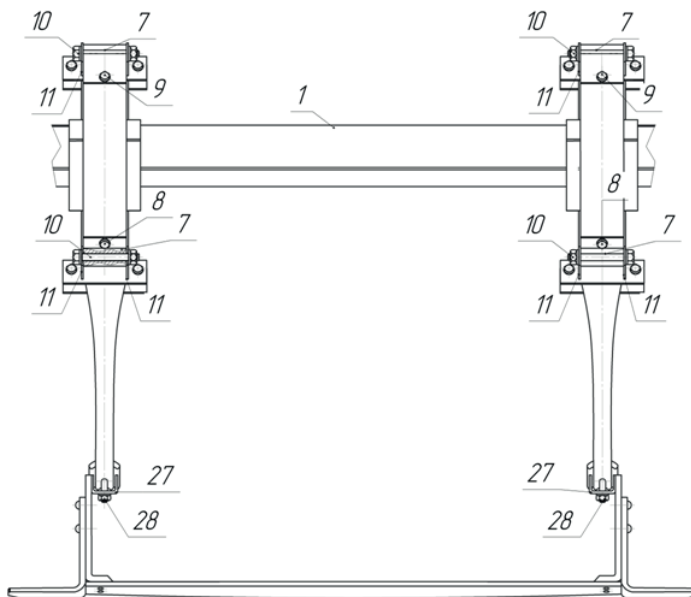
Упругий рабочий орган культиватора-плоскореза (вид спереди)
